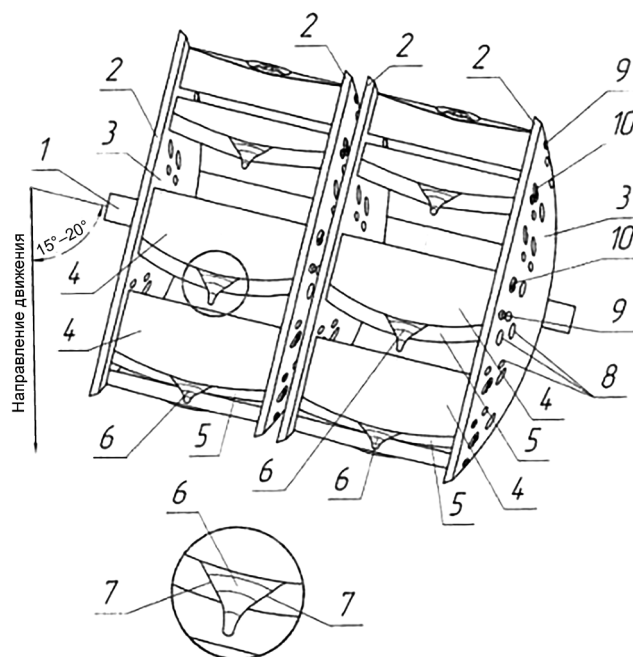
Схема рабочего органа дискового лушителя: 1 – ось; 2 – сферический диск; 3 – наружная окружность; 4 – нож; 5 – режущая кромка; 6 – вершина ножа; 7 – боковая поверхность ножа; 8 – установочное отверстие; 9 – стопорный палец; 10 – болтовое соединение
